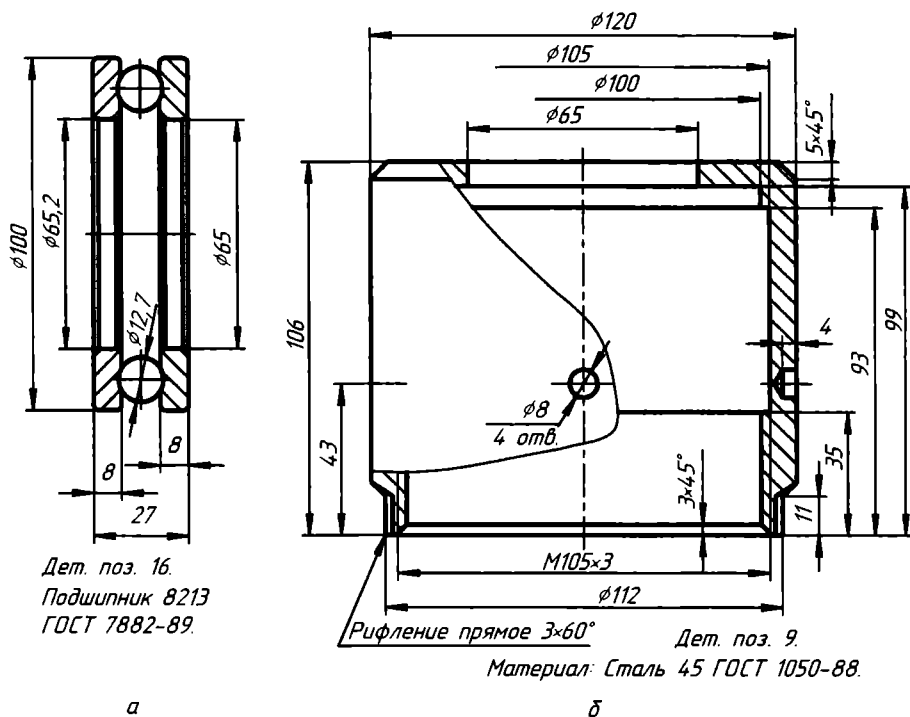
Чертежи: а — подшипника; б — гайки
